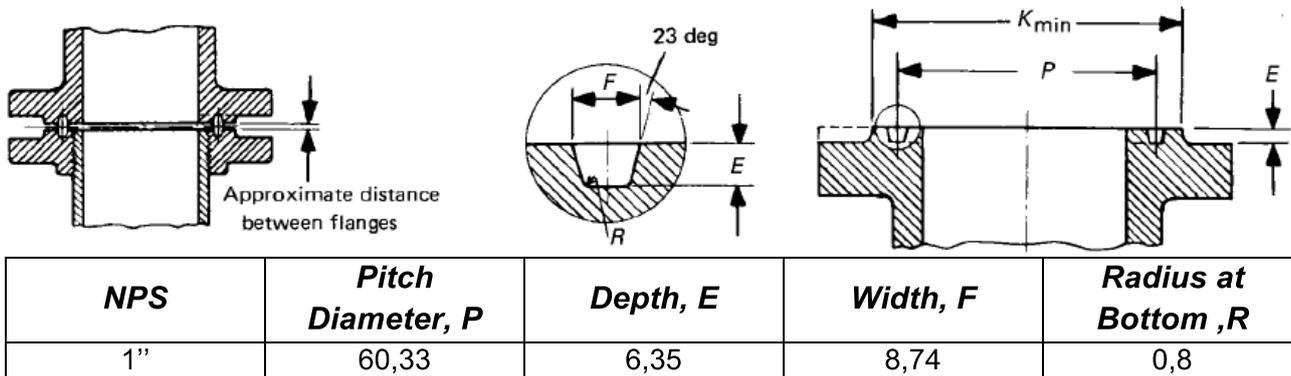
Dimensionamento flange RJT NPS 1" classe 2500, ASME B16.5
